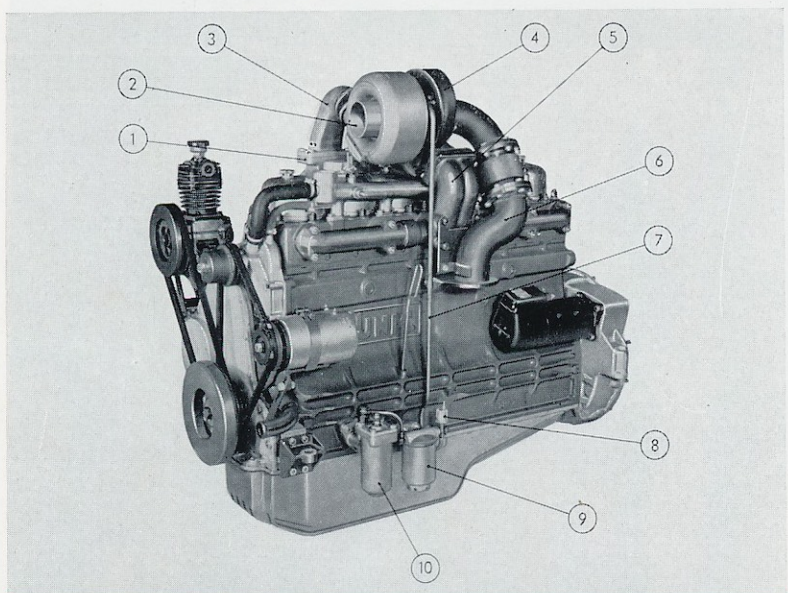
Vue d'ensemble 3/4 gauche d'un moteur 6 cylindres équipé d'un turbo-compresseur.
